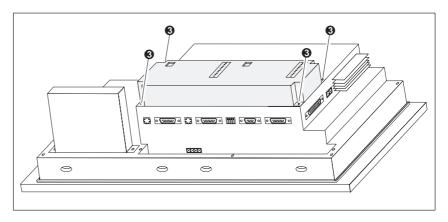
Direkttastenmodul am OP befestigen (Beispiel OP37)
